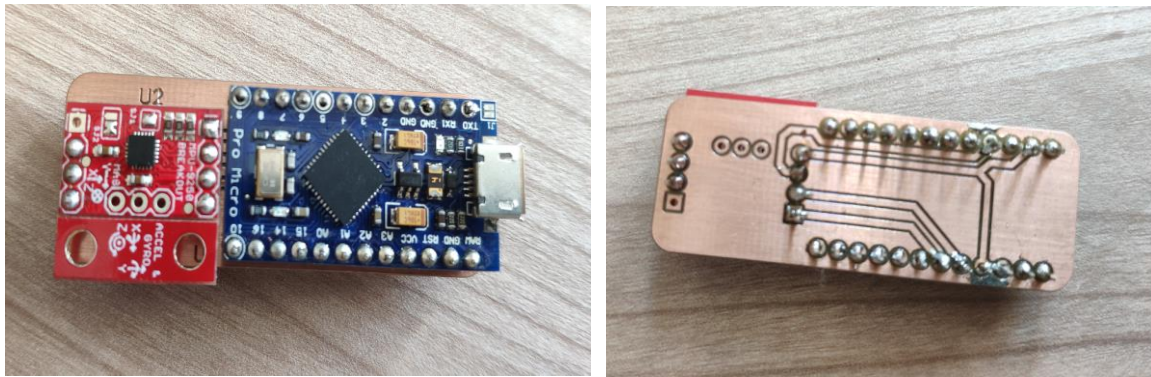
ATmega32U4 y MPU 9250 soldados en la nueva PCB
